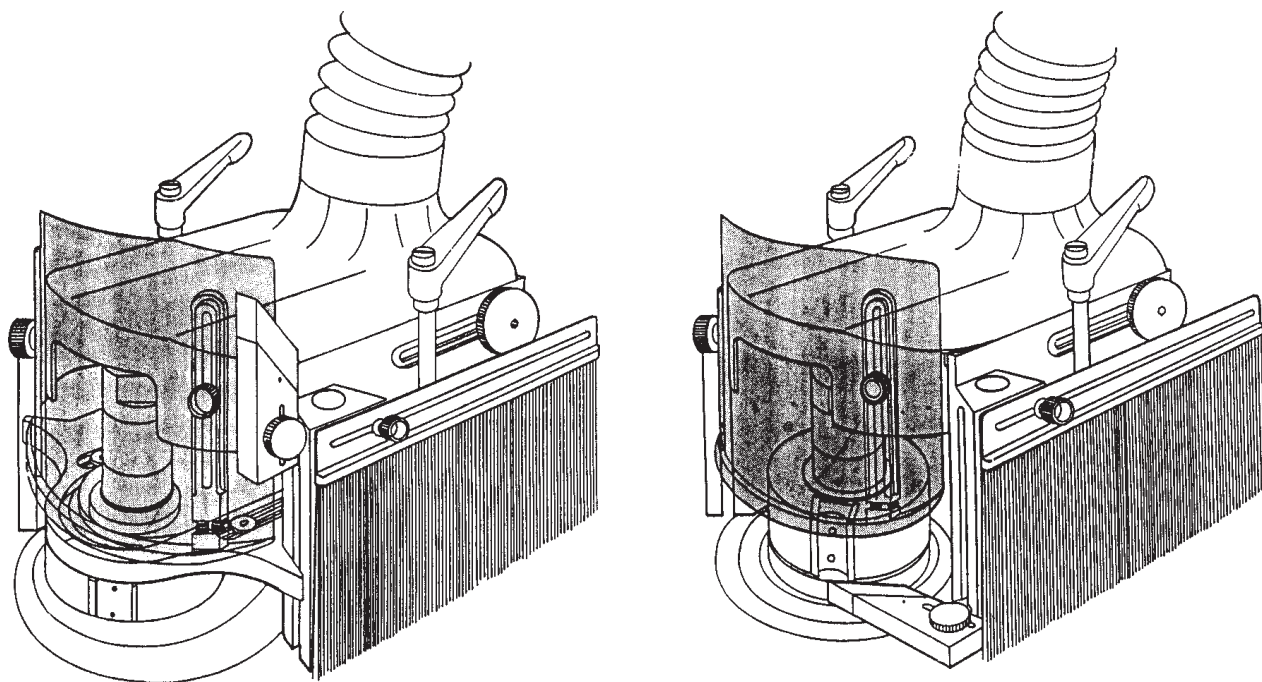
Beispiel für Werkstückführungen zum Bogenfräsen
